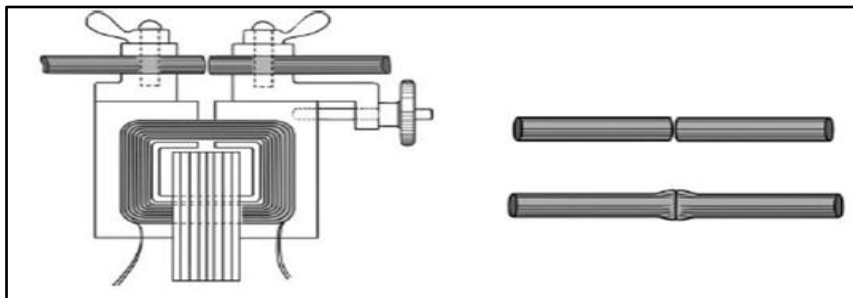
Transformateur de THOMSON pour le soudage électrique par résistance.
